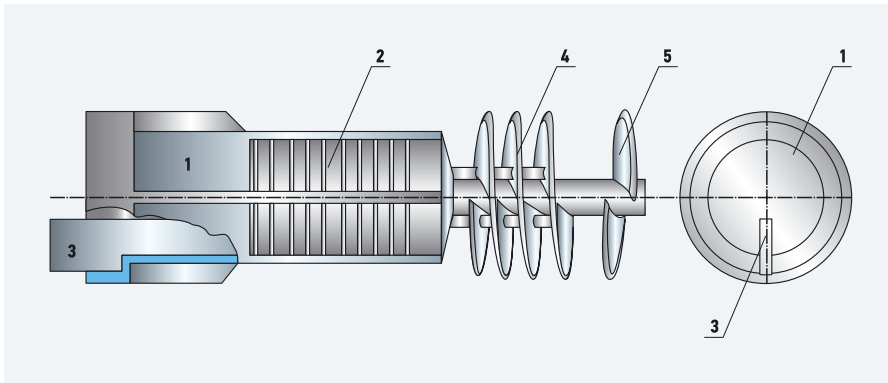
Конструктивная схема фильтра наполнительной арматуры фирмы Wirquin (1 — корпус; 2 — поперечные щели; 3 — оребренный захват; 4 и 5 — винтообразные поверхности)
